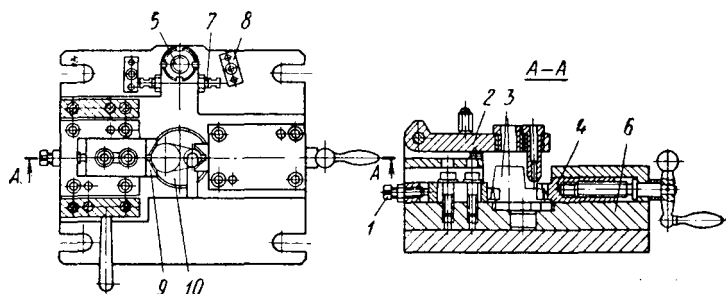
Приспособление поворотное для обработки отверстий в рычагах небольших размеров
